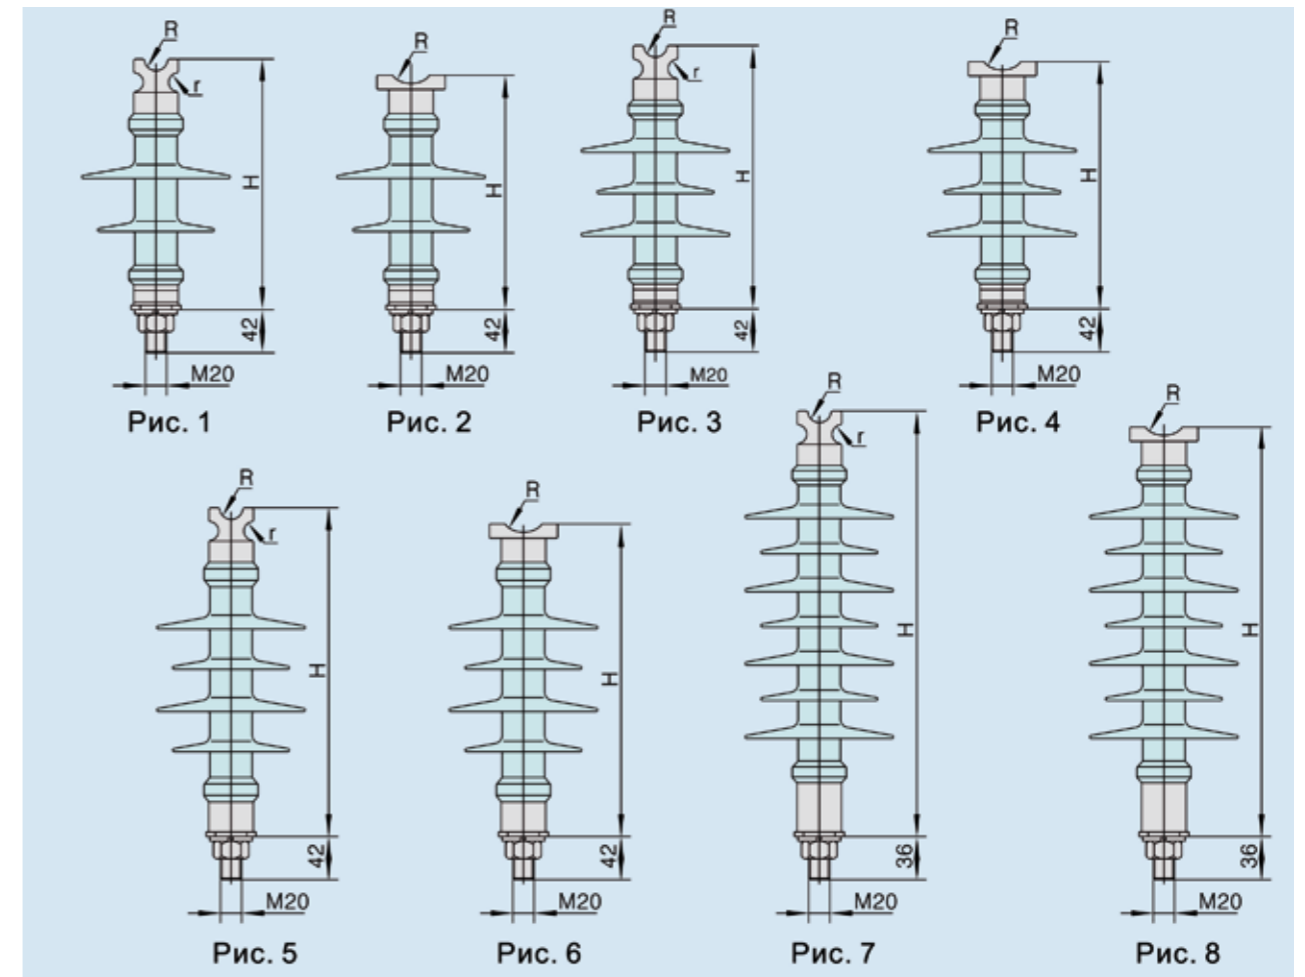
Внешний вид и размеры комбинированных штыревых изоляторов
